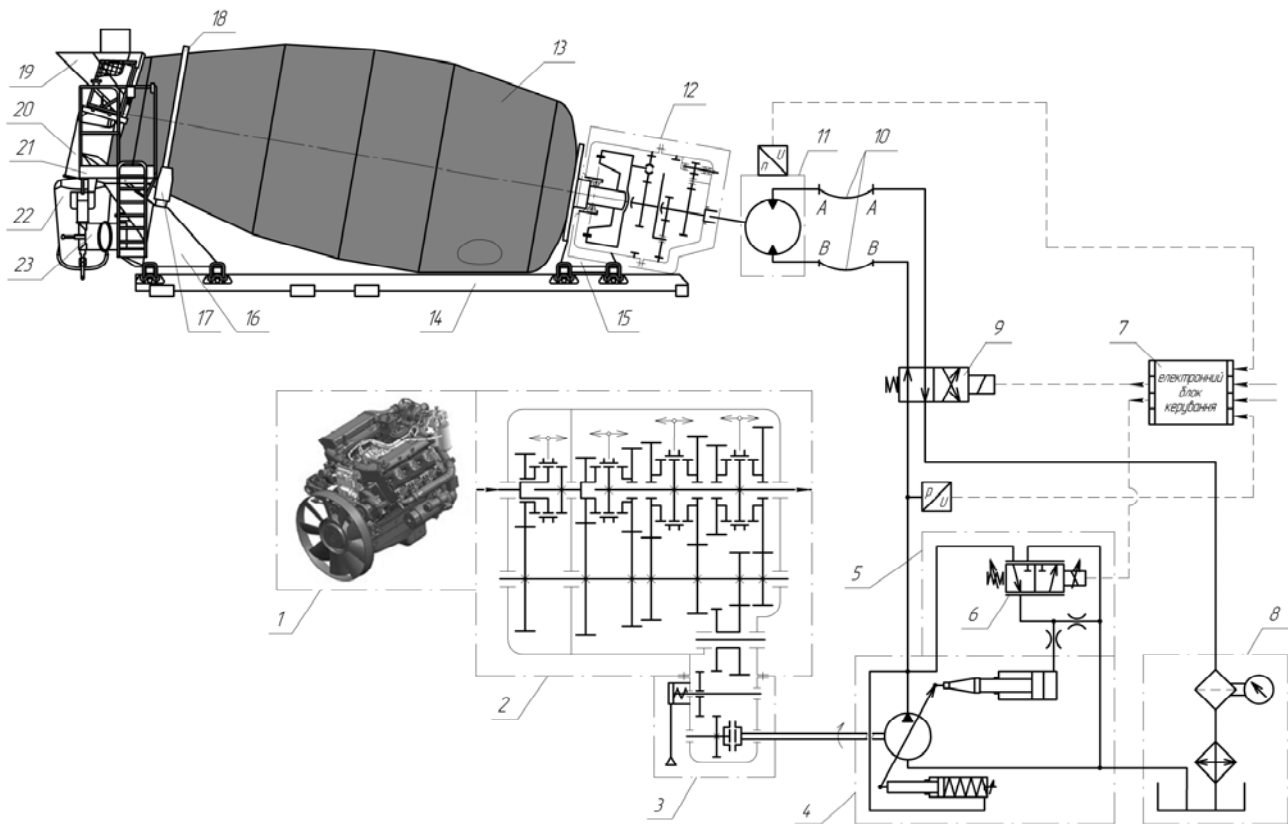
Принципова схема приводу обертання змішувального барабана АБЗ:
